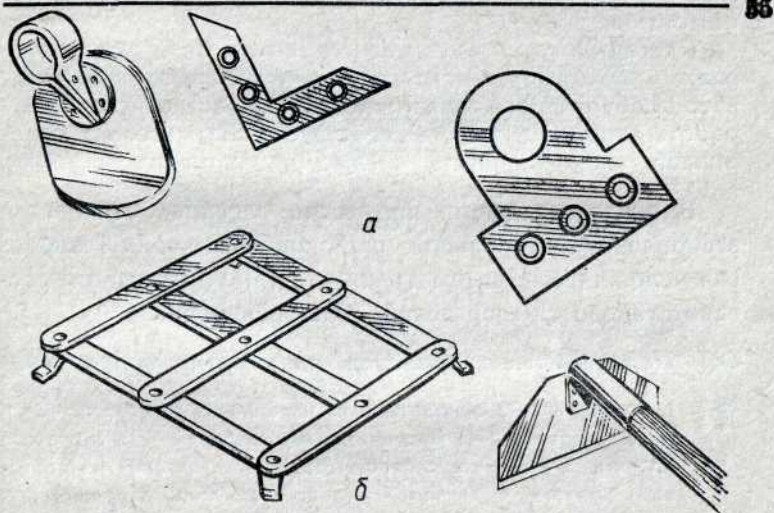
Изделия из сортового проката: а — однодетальные; б — многодетальные.
